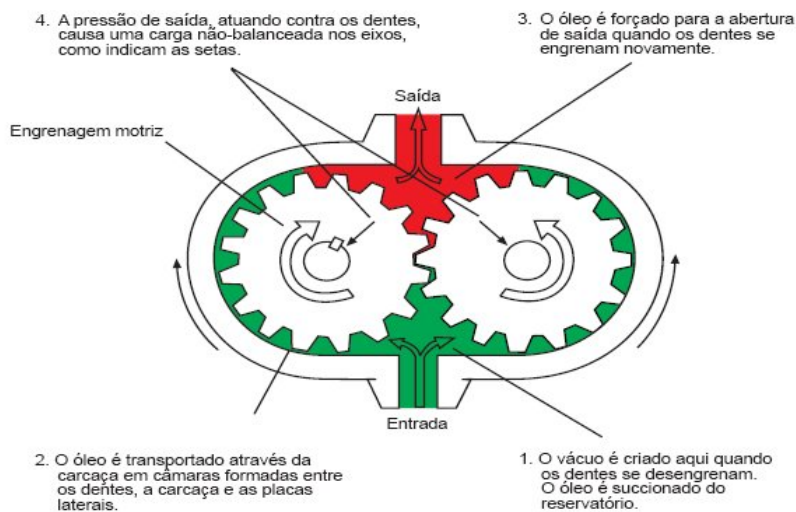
Exemplo de uma bomba de engrenagem externa.
